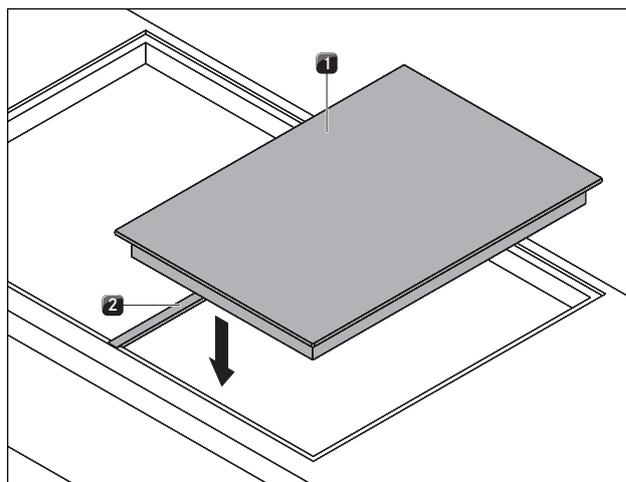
Colocar la guía de montaje y la placa de cocción
